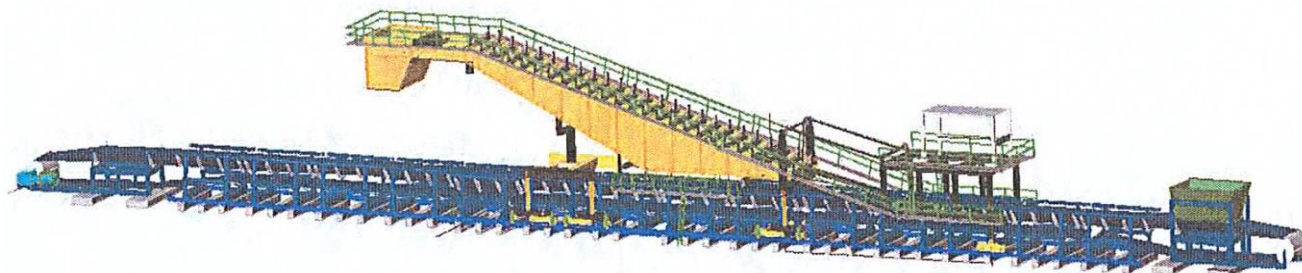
Общий вид ленточно-петлевого перегружателя и ленточного конвейера
